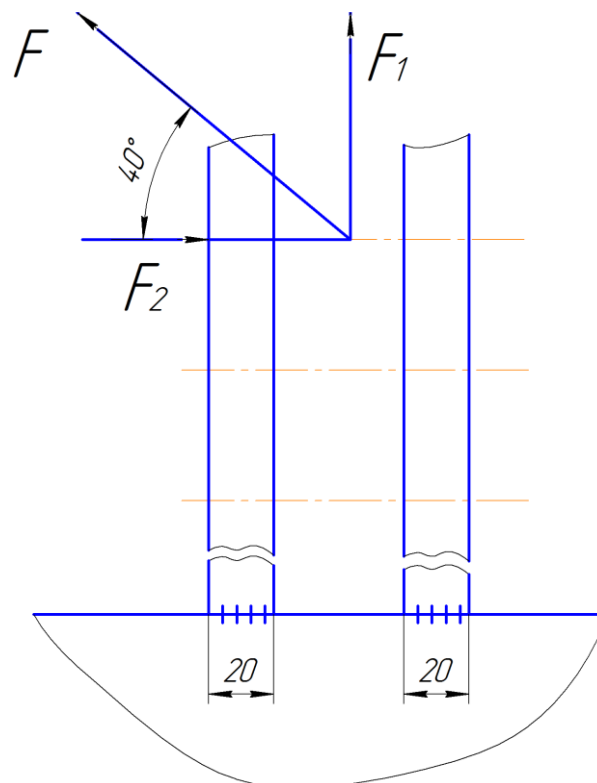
Розрахункова схема зварного шва кронштейна регулювальної планки
